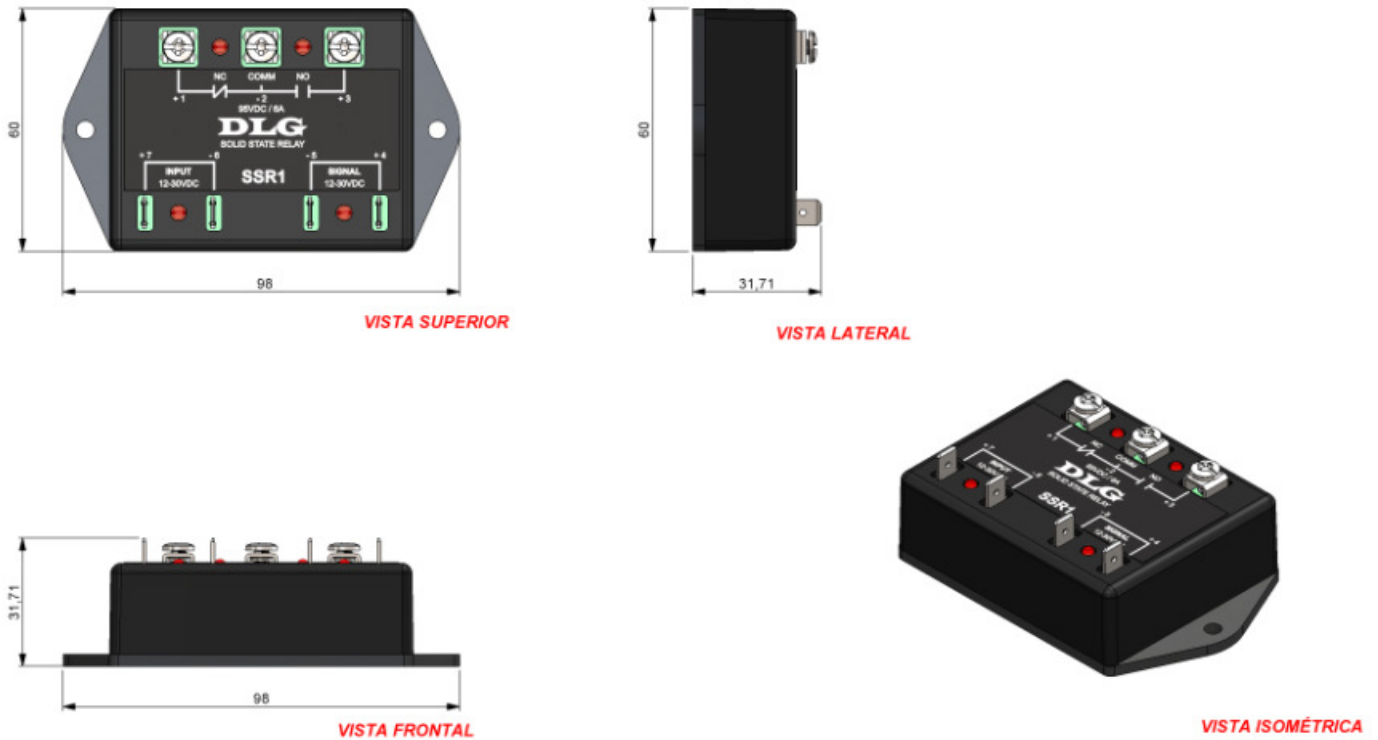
Dimensionamento para montagem (Cotas em milímetro)
